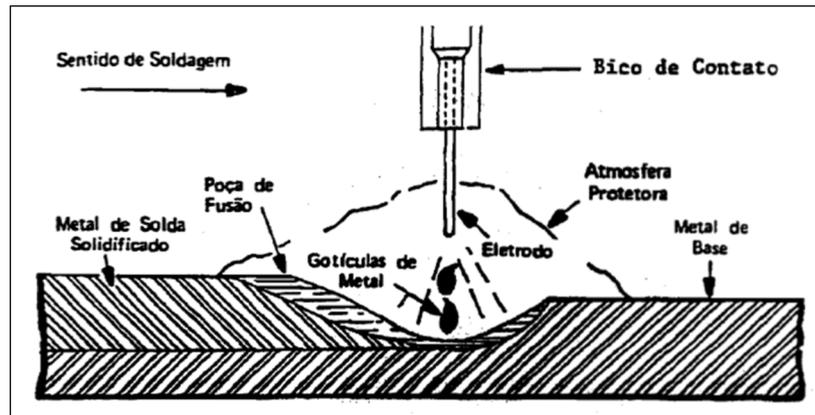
Processo de Soldagem – FCAW (LUZ, 2018).
